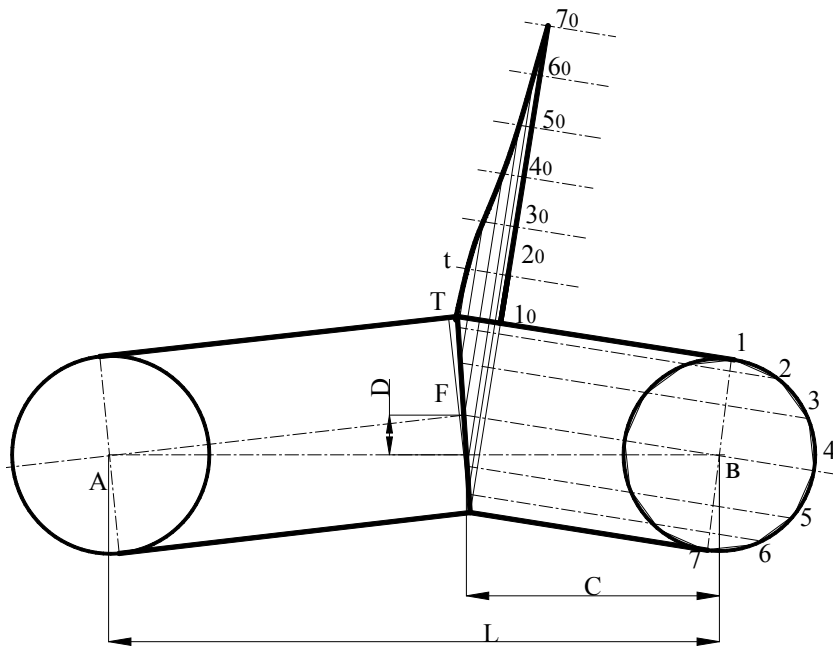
Схема викривлення циліндричного корпусу
